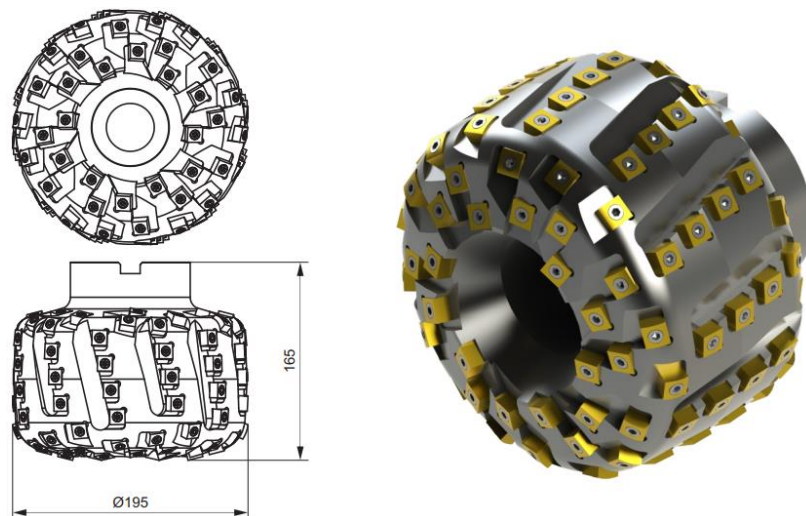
Сборная фасонная фреза для восстановления боковых бочкообразных профилей рельса фирмы CORUN, Сербия.
